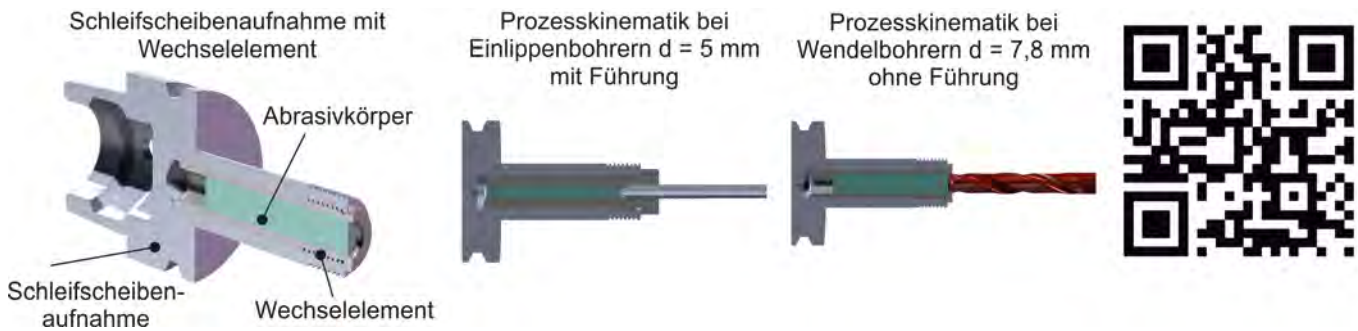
Integration der Werkzeugpräparation auf Werkzeugschleifmaschinen durch [Tool]Prep
